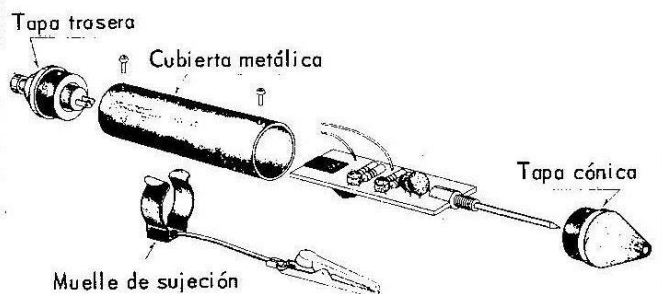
Despiece y disposición de montaje del inyector de señales.
